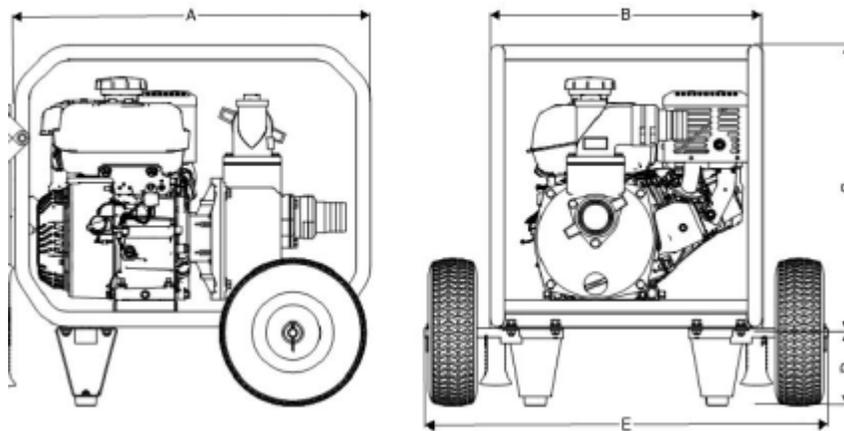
Medidas Marco de MotoBomba Diseño III
